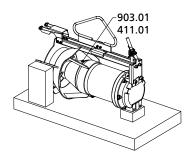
Llenado del líquido lubricante; Amaline 300 con motor 86
